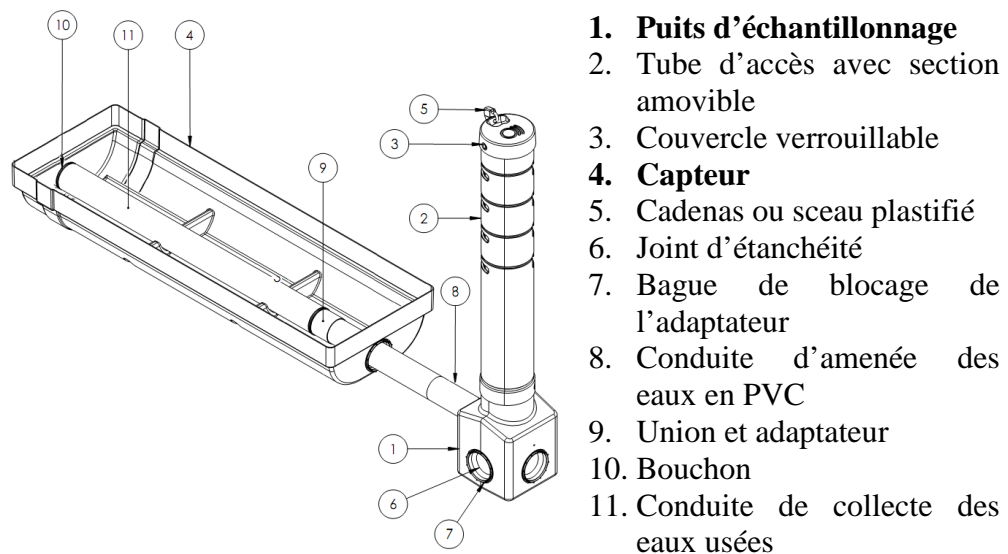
Vue d'ensemble du dispositif d'échantillonnage
